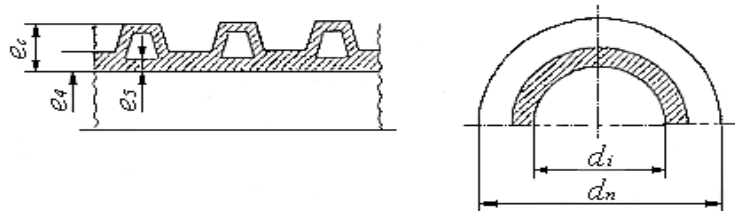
Продольный и поперечное сечение труб типа В (без раструба) в конструктивном исполнении с гофрированной поверхностью и гладкой части труб раструбных типа В
